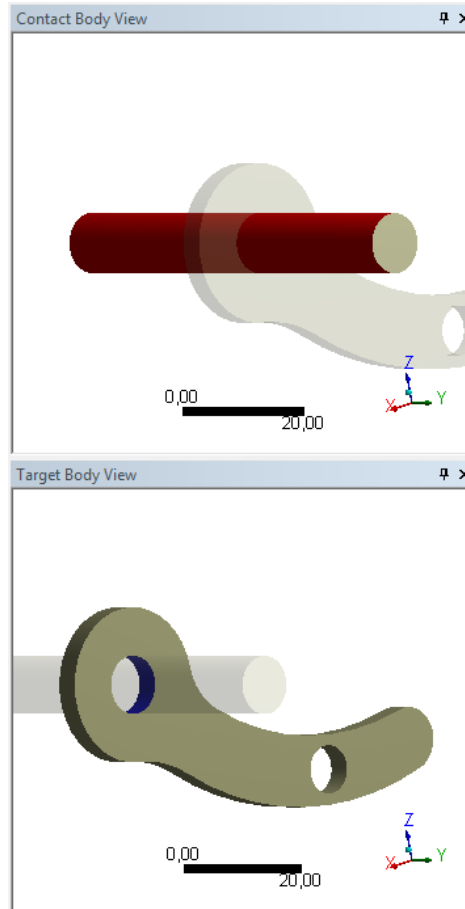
Contacto tipo frictionless entre pasador y placa de aluminio
